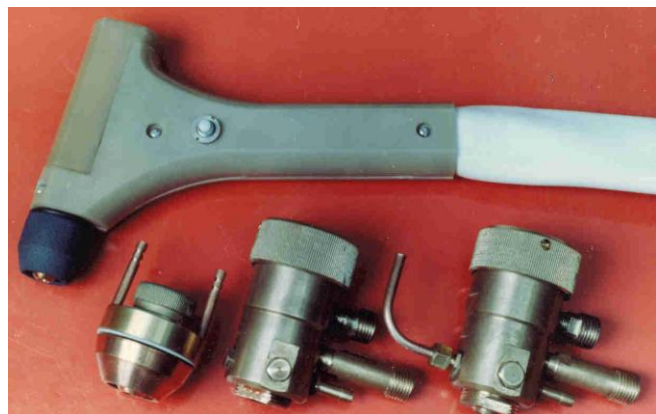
Установка плазменной сварки, наплавки, напыления, закалки и финишного плазменного упрочнения
